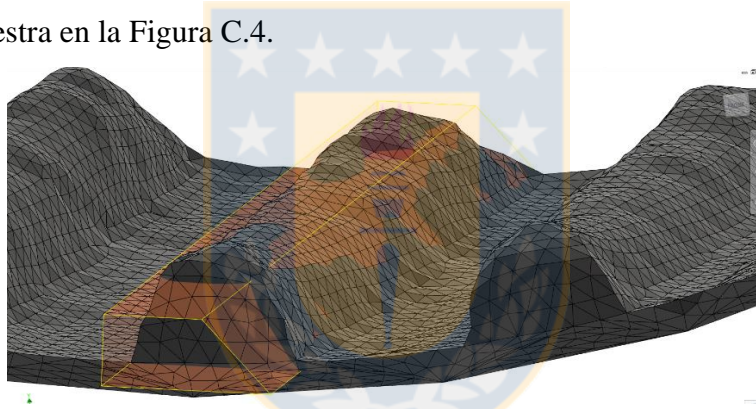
Superposición de superficie rectangular sobre cara de ataque de alizador desgastado (Fuente: Elaboración propia).
